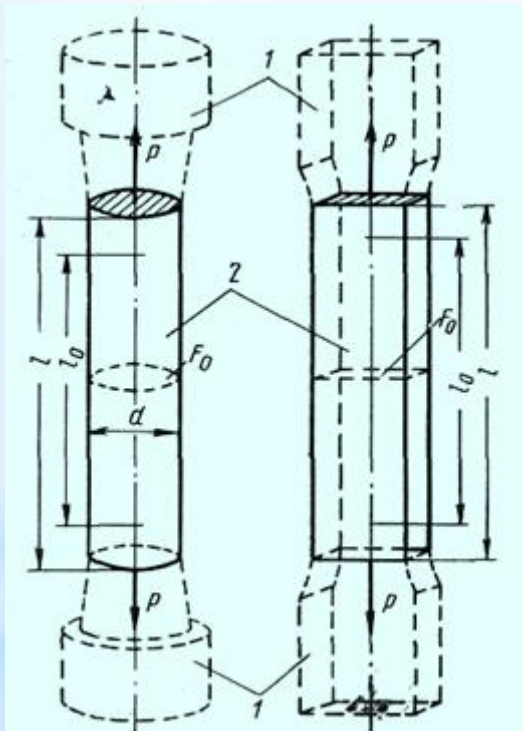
Зразки для випробування розтягування: 1 – головки; 2 – робоча частина
